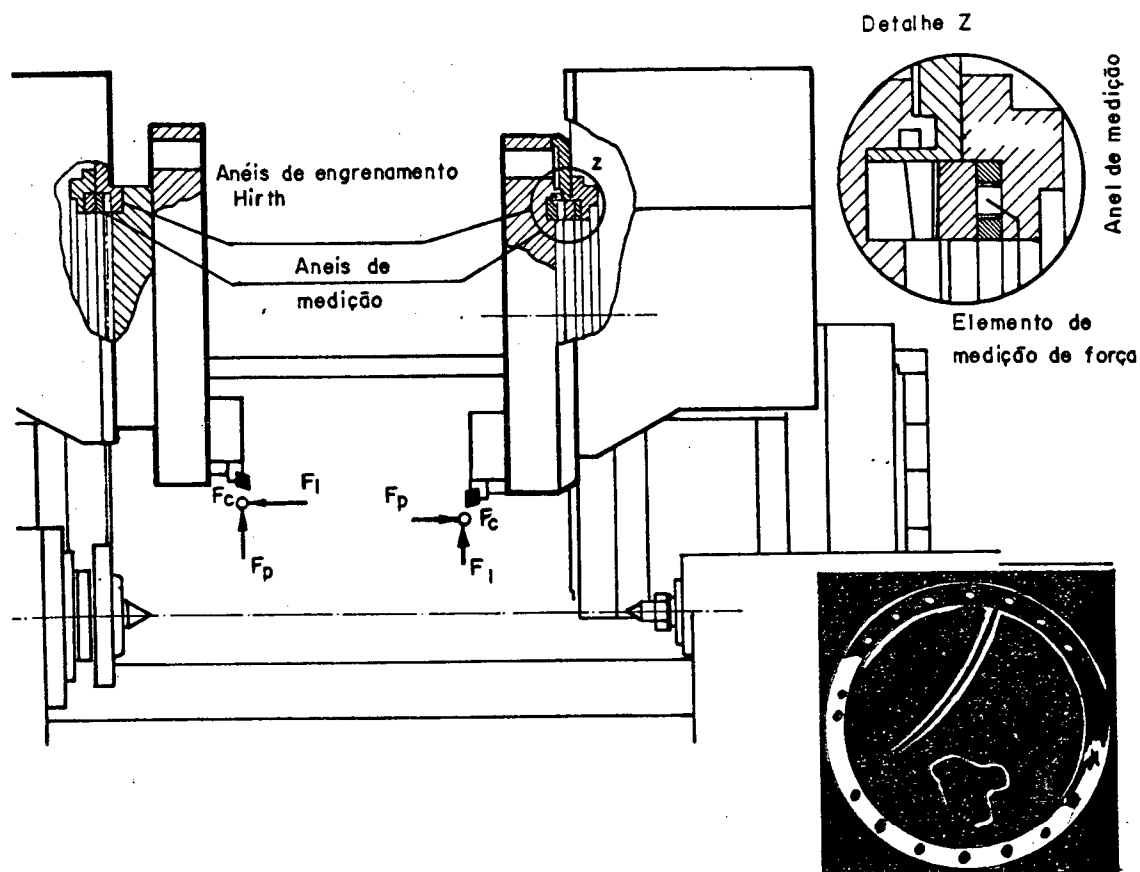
Anéis de medição para medição de força em um torno 4 eixos CNC [9,73].
